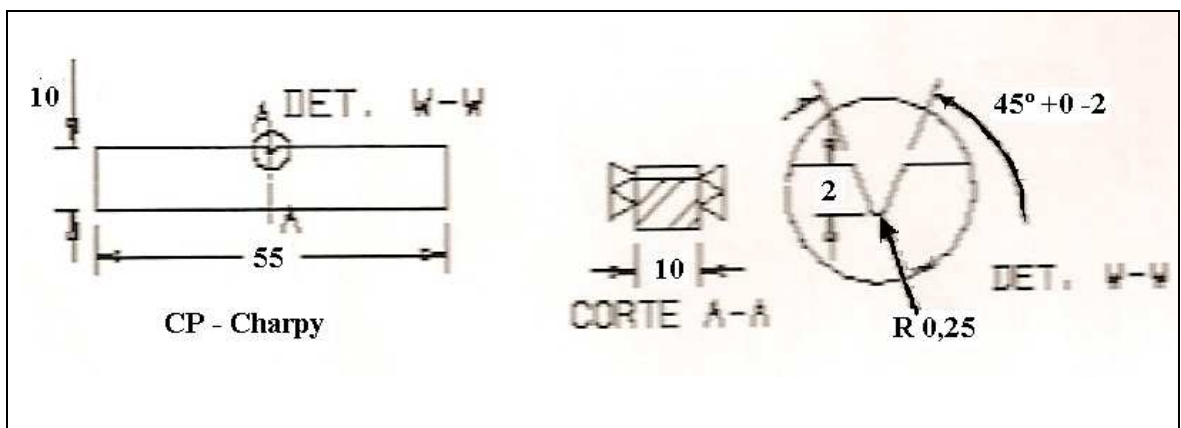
Desenho do corpo de prova de ensaio de impacto Charpy – ASTM E-23
